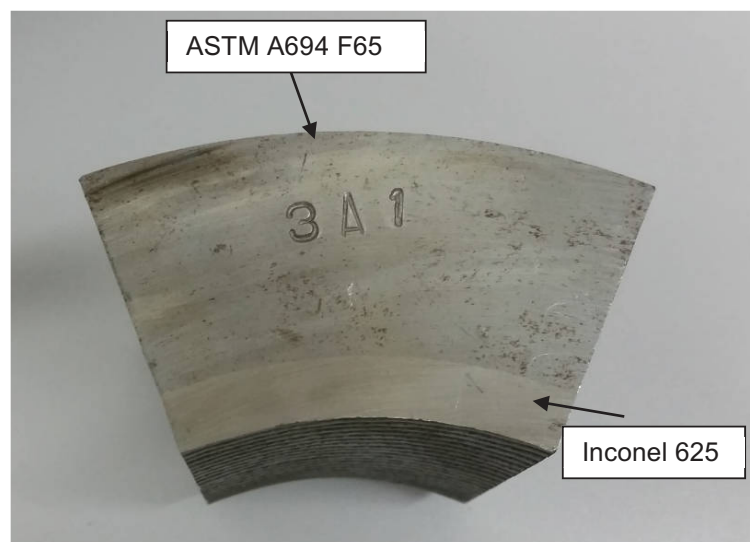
Arco retirado da seção transversal do tubo na condição como soldado.
